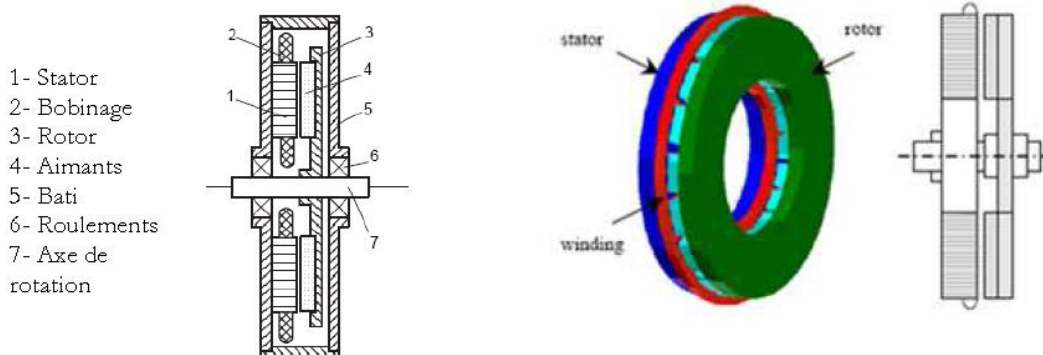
Machine à flux axial 1 stator / 1 rotor. [16]
